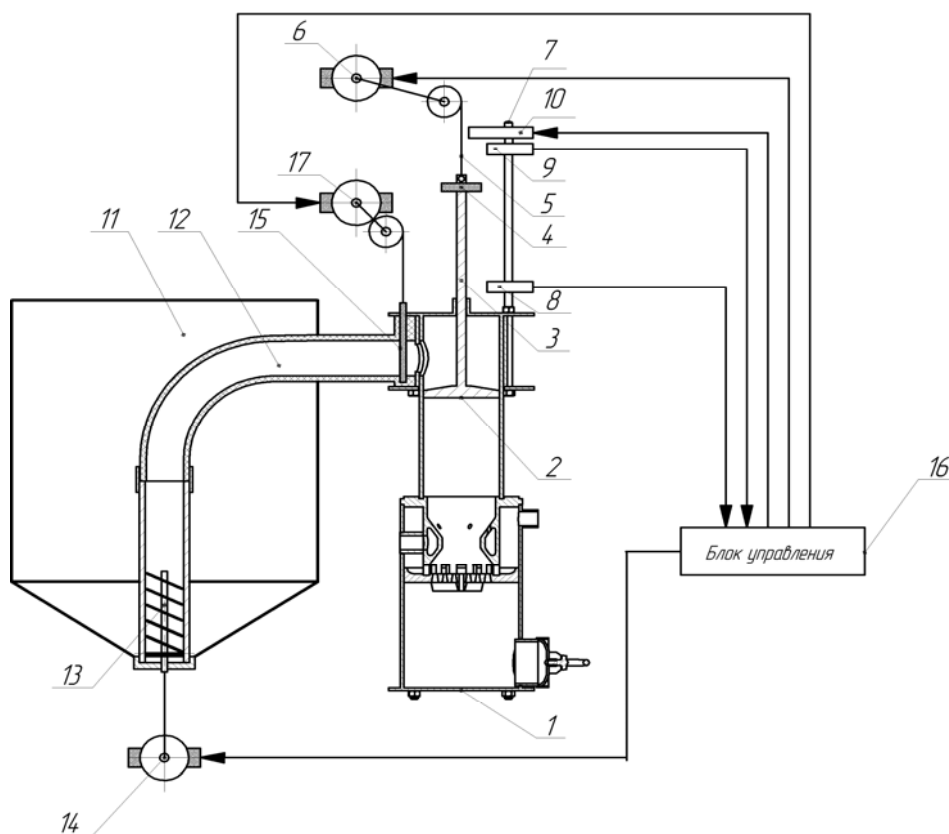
Газогенератор непрерывного действия: 1 – корпус; 2 – поршень; 3 – шток; 4 – магнит; 5 – трос гибкий; 6 – механизм подъемный; 7 – штанга; 8 – датчик нижнего положения уровня топлива; 9 – датчик верхнего положения уровня топлива; 10 – механизм стопорный; 11 – бункер; 12 – Шнековый канал; 13 – шнек приводной; 14 – электродвигатель; 15 – заслонка электромеханическая; 16 – блок управления; 17 – электропривод
